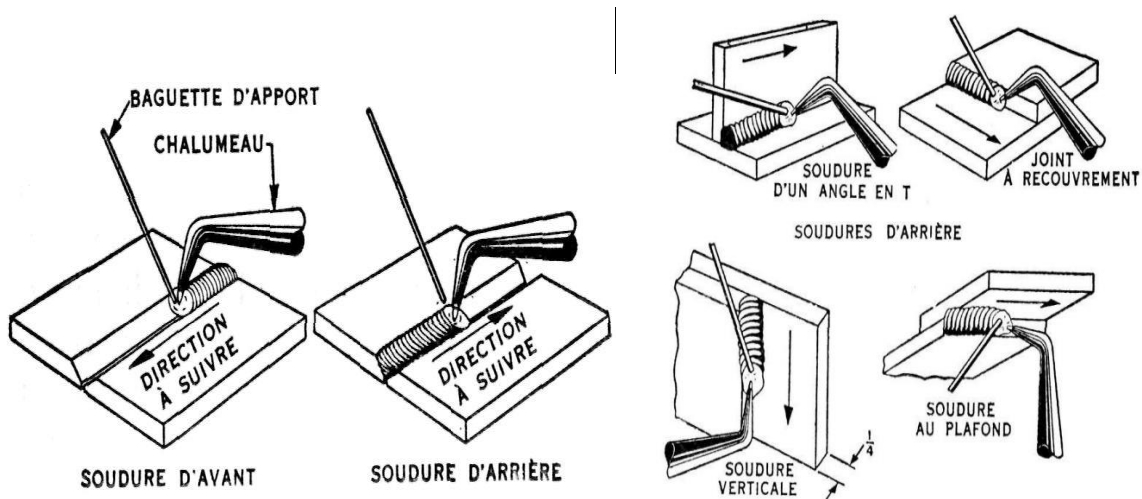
types de soudures exécutées au chalumeau
